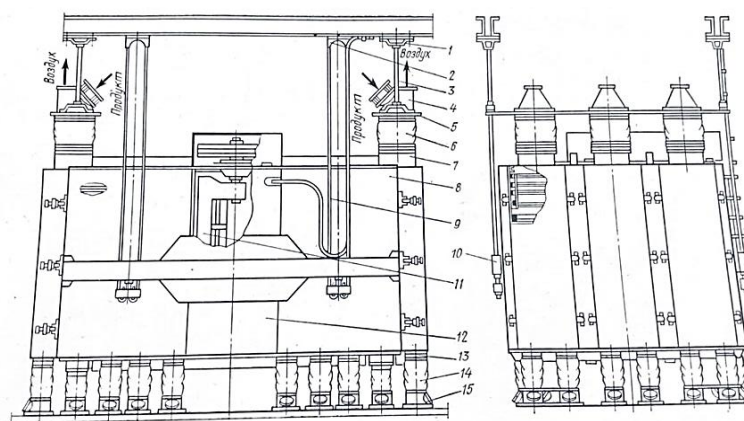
Рассев ЗРШ-6М: 1-державка; 2-подвеска; 3-валик-штанга; 4-приемная коробка; 5- приемная доска; 6-приемный рукав; 7-приемный патрубок; 8-ситовый корпус; 9- канат; 10-замок; 11-дебалансный колебатель; 12-ограждение; 13-выпускной патрубок; 14-рукав; 15-напольный патрубок
